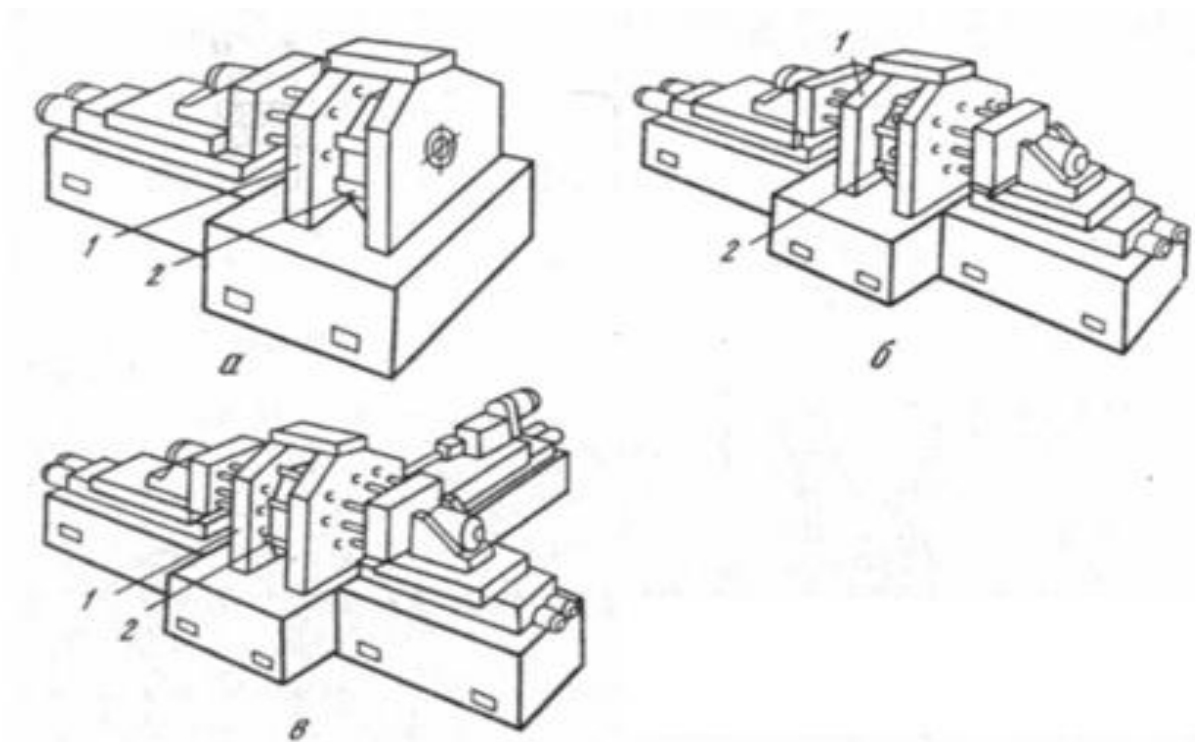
Типовые компоновки агрегатных станков с поворотным делительным барабаном.
